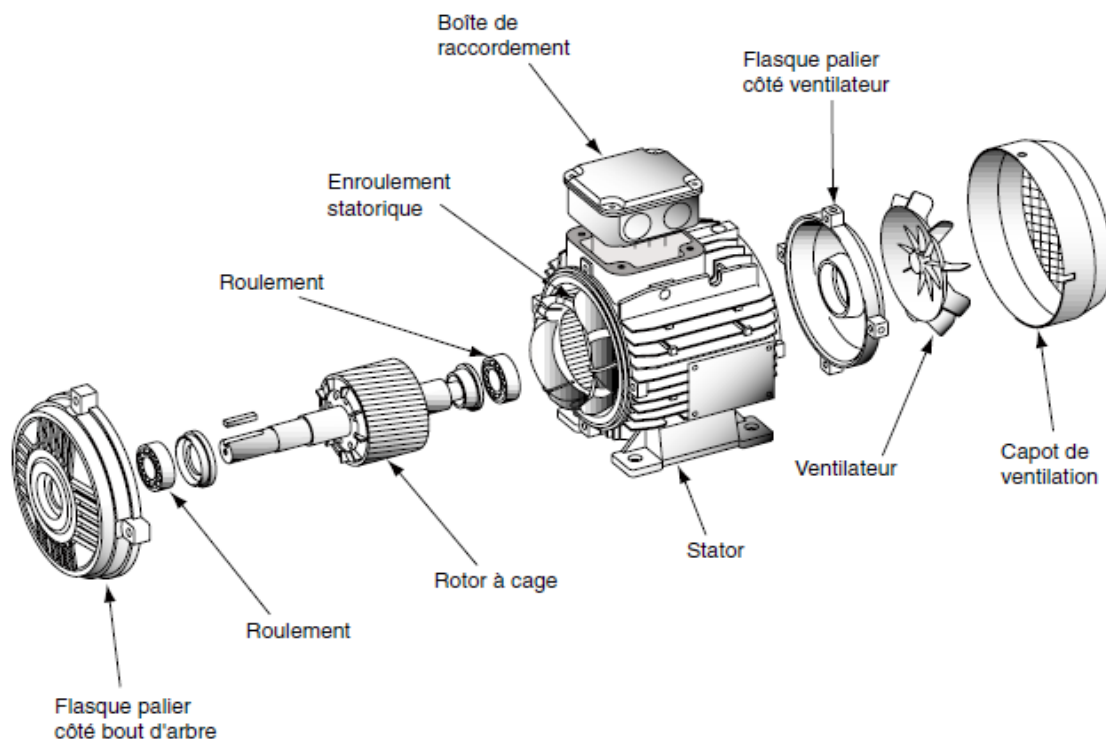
Vue éclatée d'un moteur asynchrone triphasé à cage.
